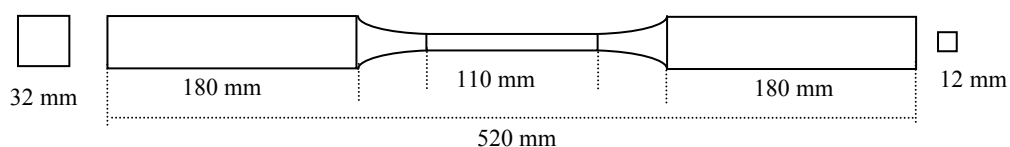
Dimensões do provete para ensaio de tracção paralela usado para madeira de eucalipto comum.
